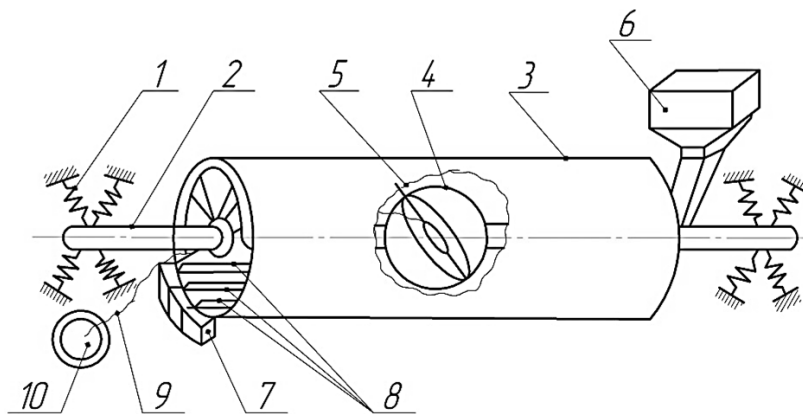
Принципова схема сепаратора з циліндричною робочою поверхнею:
